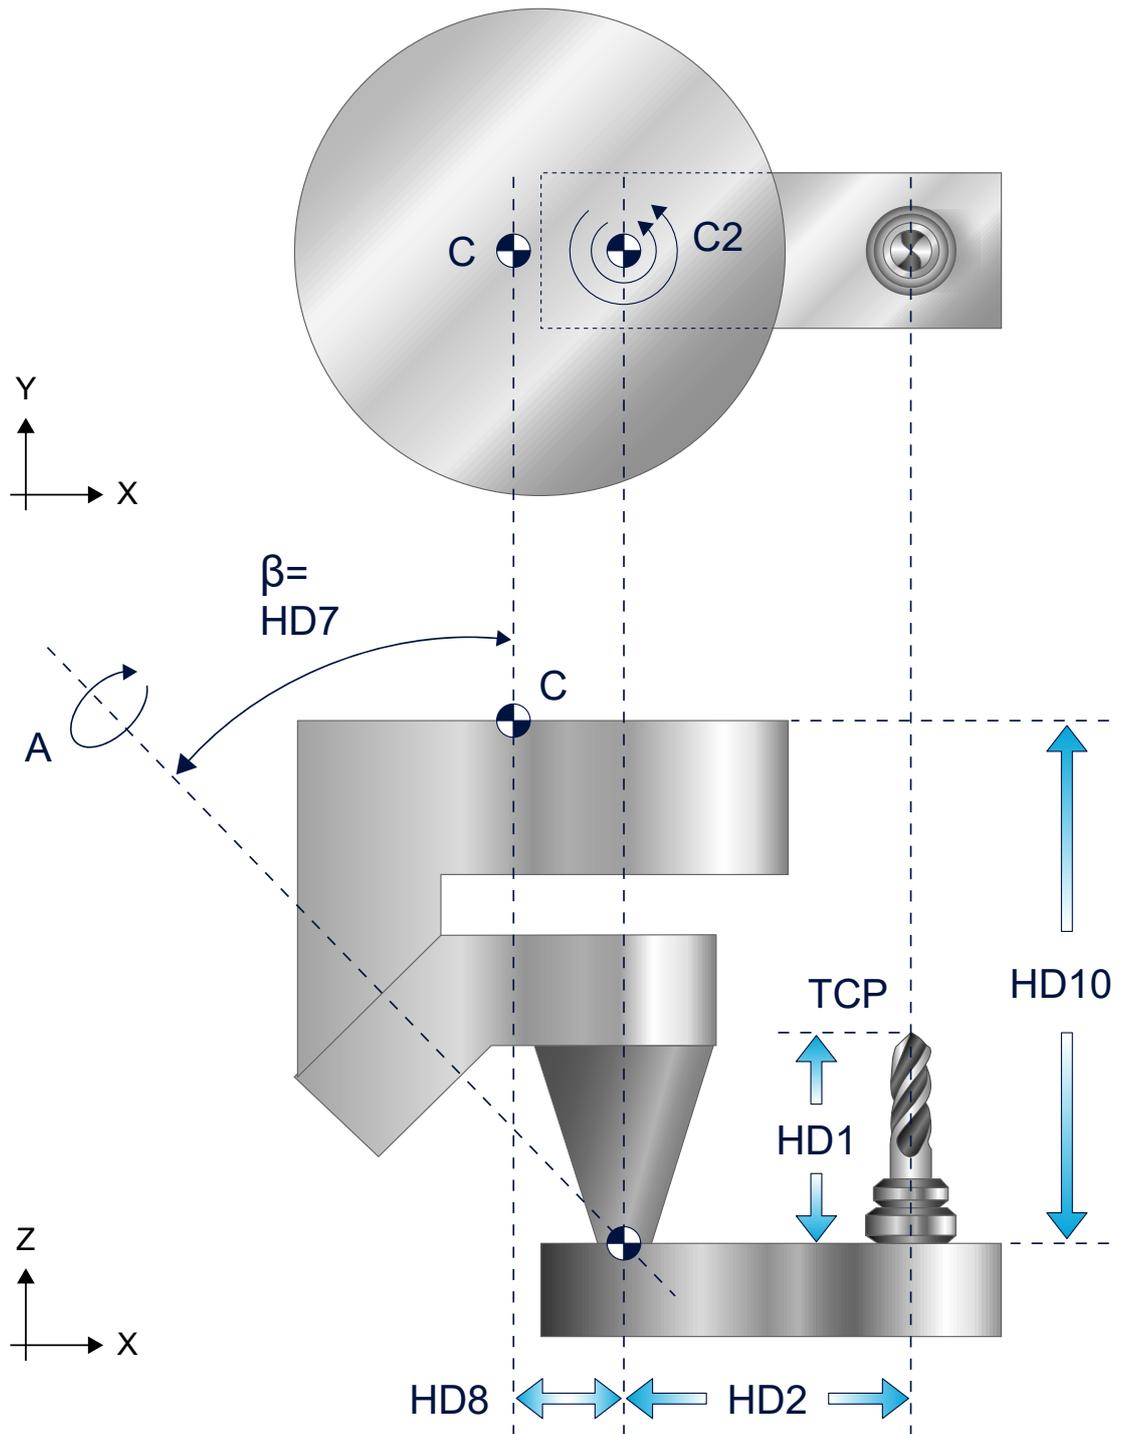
Kardankopf mit Unterflurfräser mit versetzter C-Achse
